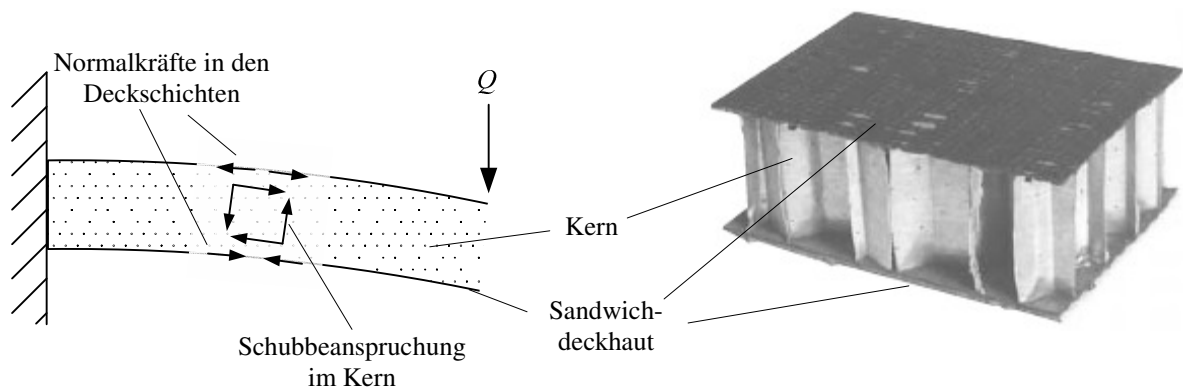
Sandwichbauweise mit kohlenstofffaserverstärkten Sandwichhäuten auf einem Aluminiumwabenkern (rechts)
